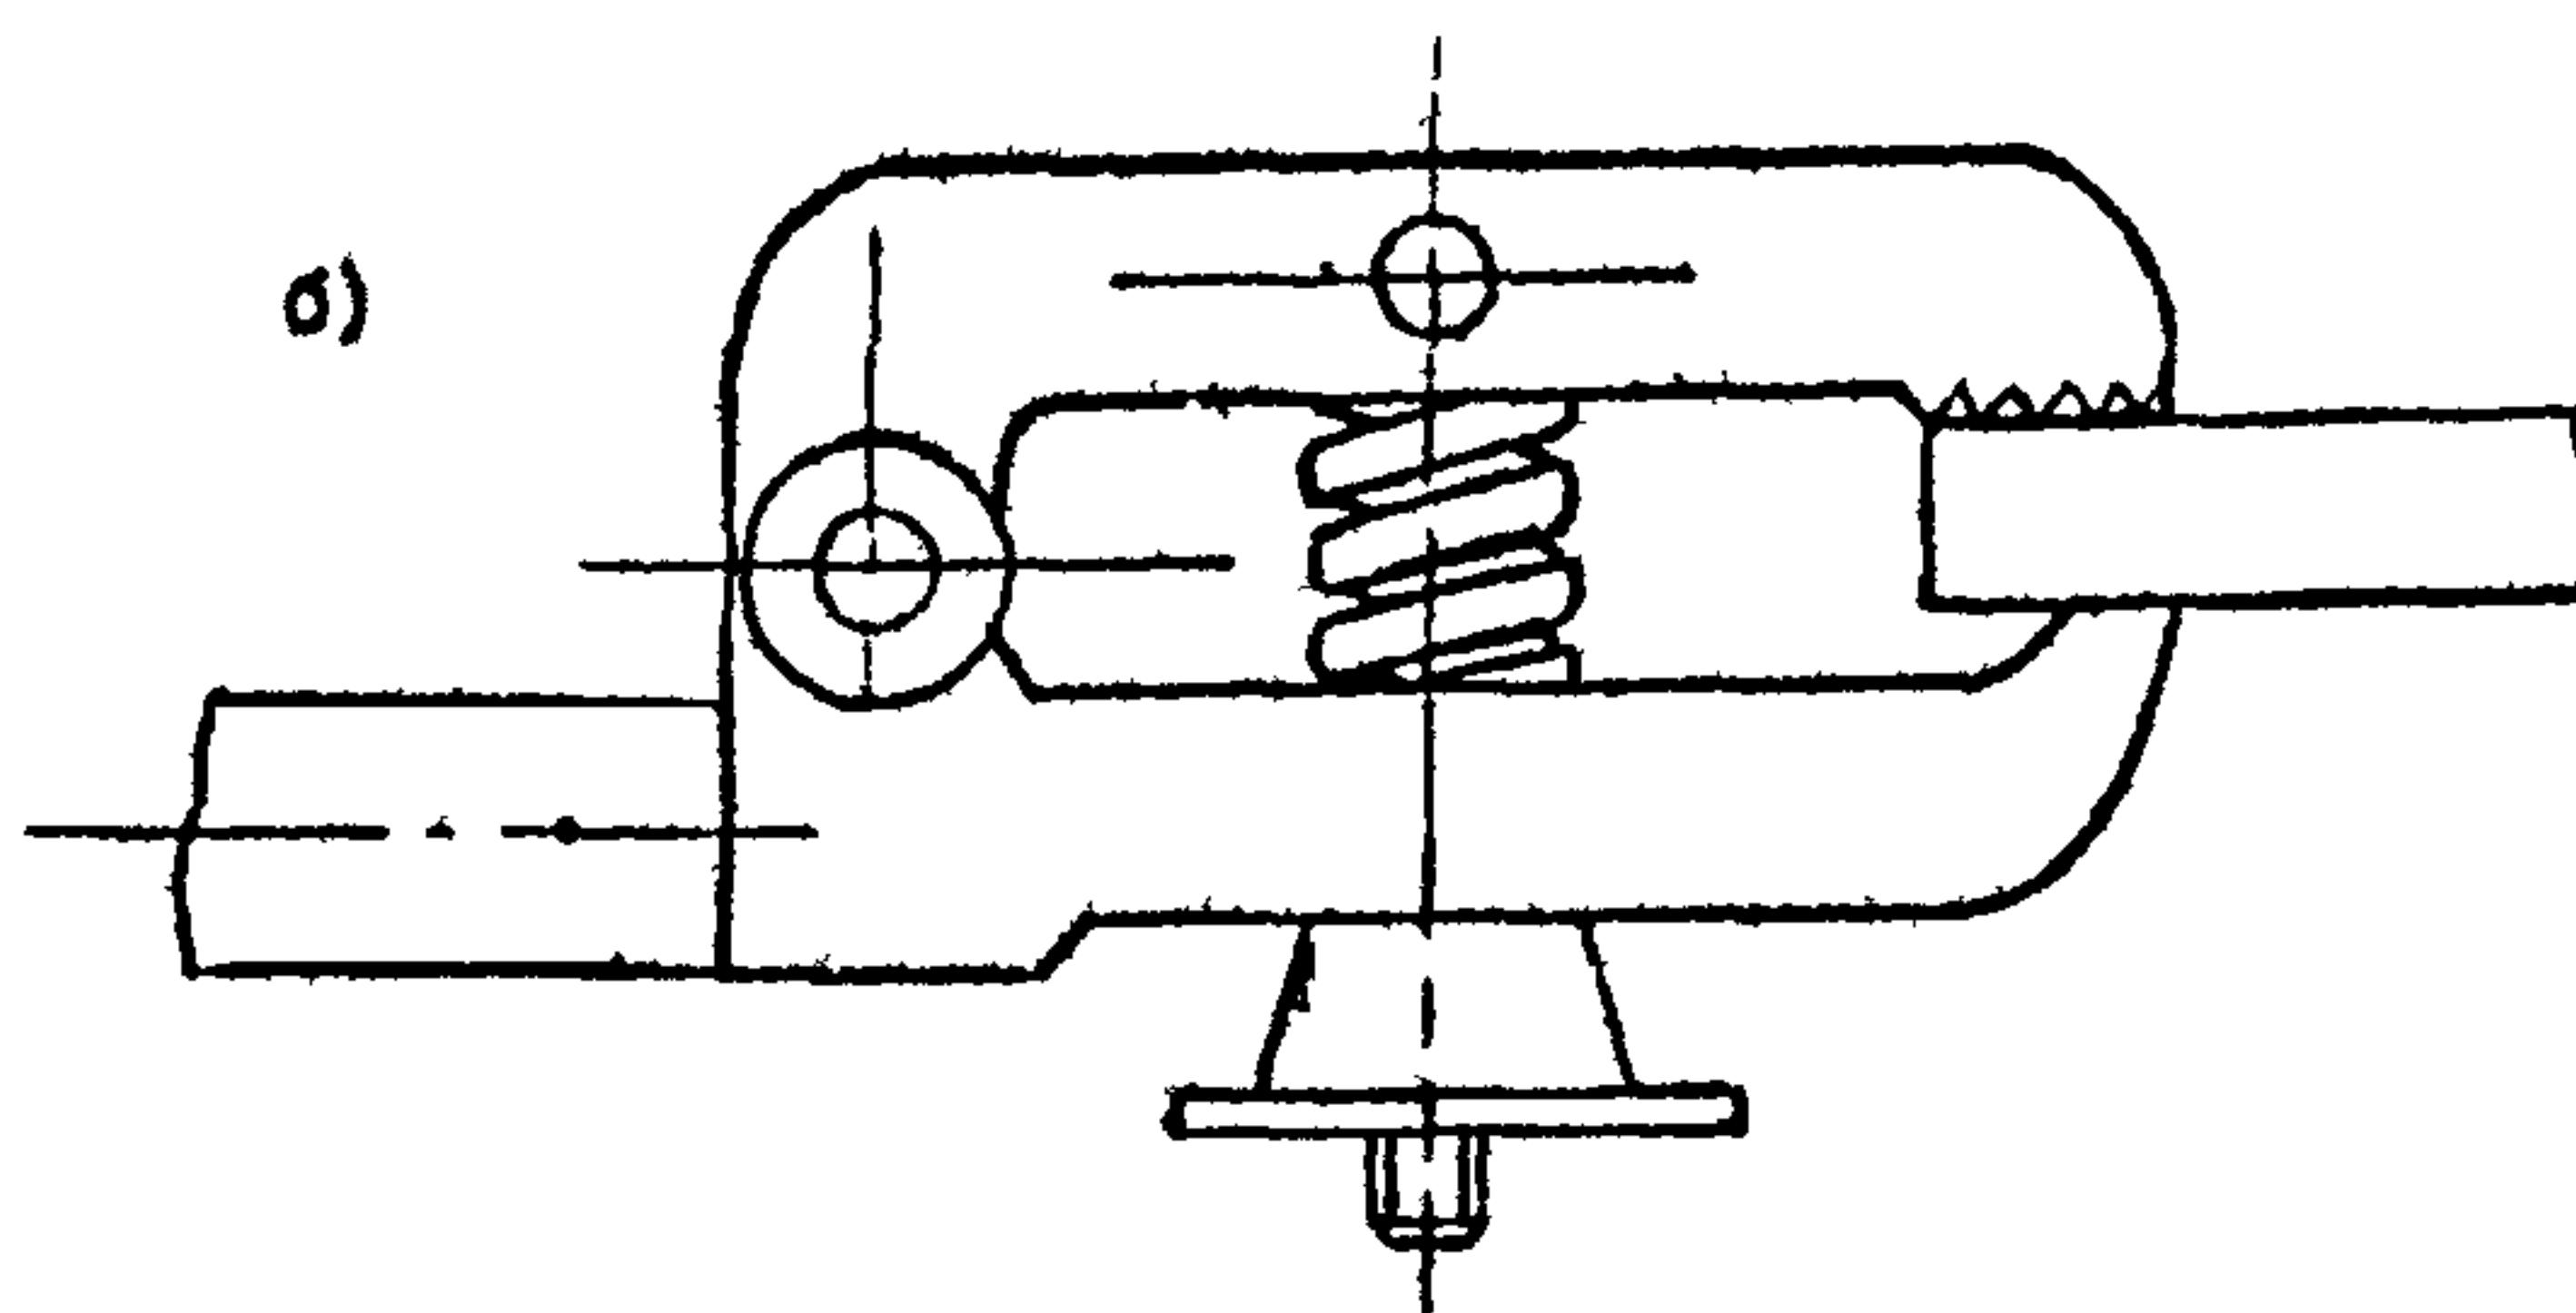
Зажимы для присоединения сварочного провода к свариваемому изделию:
